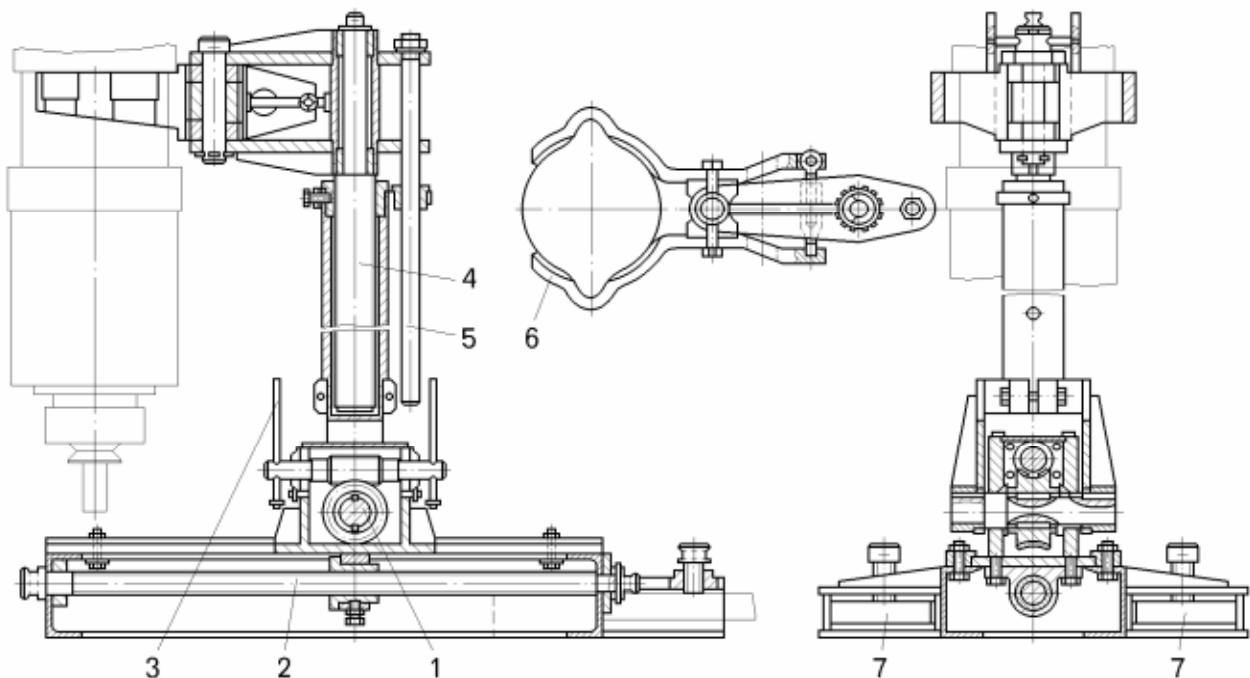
Приспособление для снятия и установки цилиндров подвески с использованием автопогрузчика:
